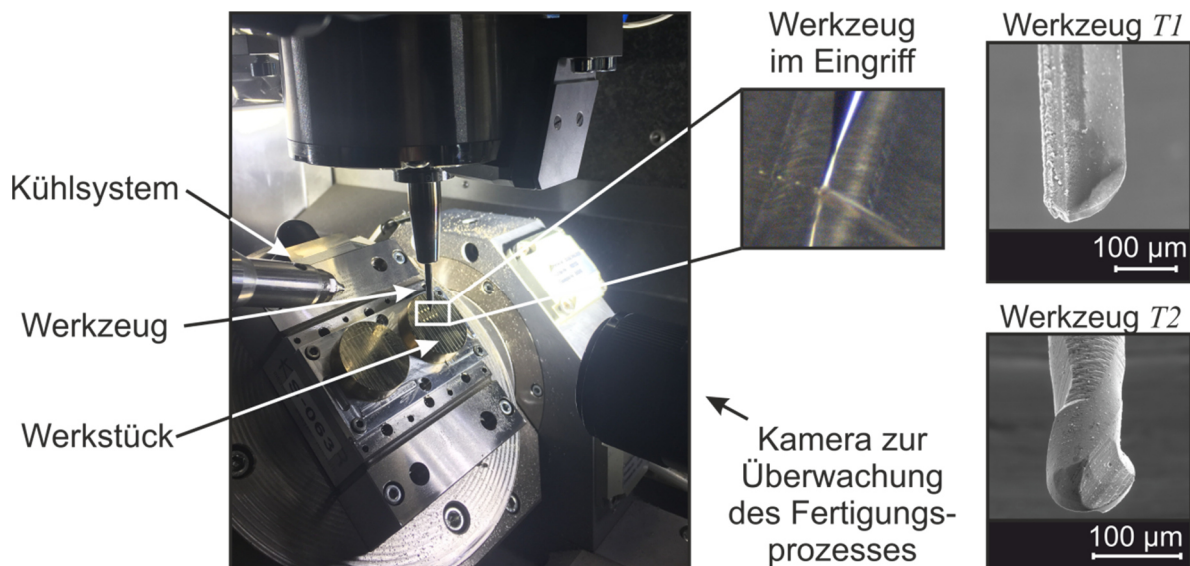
Mikrofräse LT Ultra MMC 600 H1 sowie Werkzeuge T1 und T2
